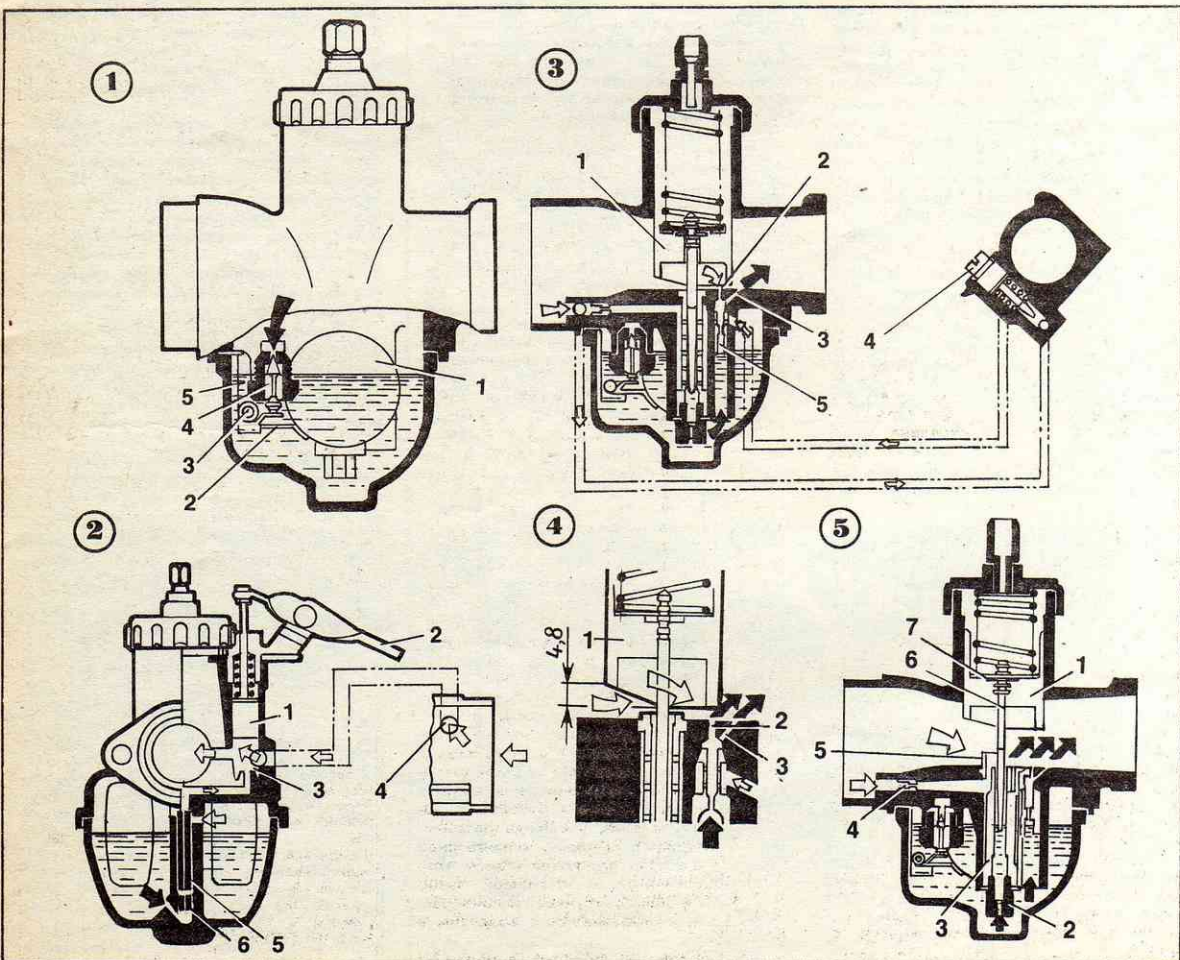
Поплавковый механизм: 1 — поплавок; 2 — рычаг; 3 — ось; 4 — игла; 5 — корпус клапана.
